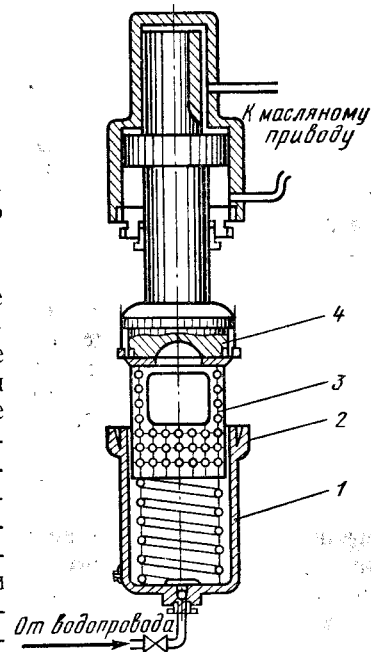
Схема установки для увлажнения деталей низа обуви под давлением
